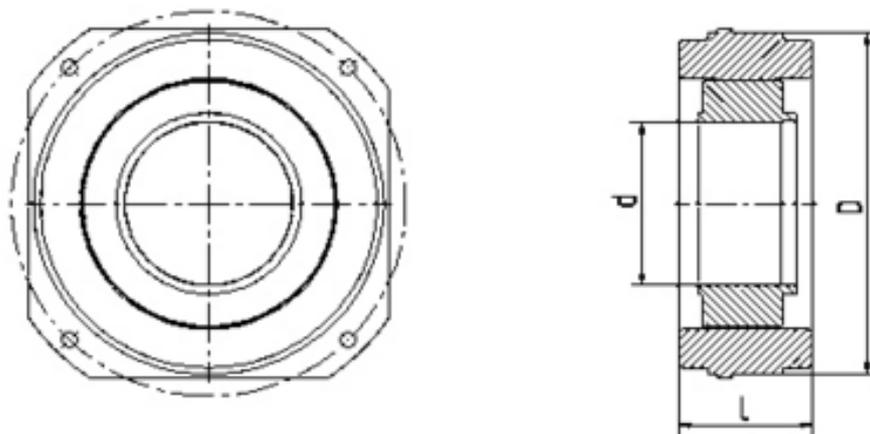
Двигатель ДБМ с пазовым статором
